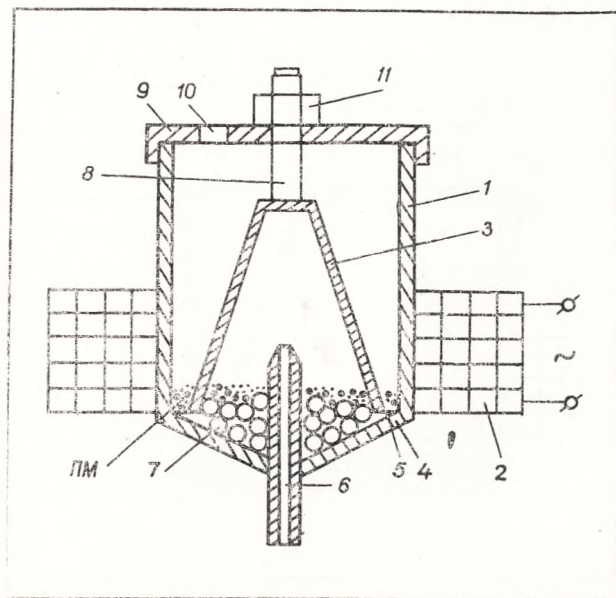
Вибратор установки типа «Разряд»: 1 — корпус; 2 — электромагнитный вибратор; 3 — регулировочная игла; 4 — стопорная гайка; 5 — сменная насадка; 6 — гайка крепления насадки
